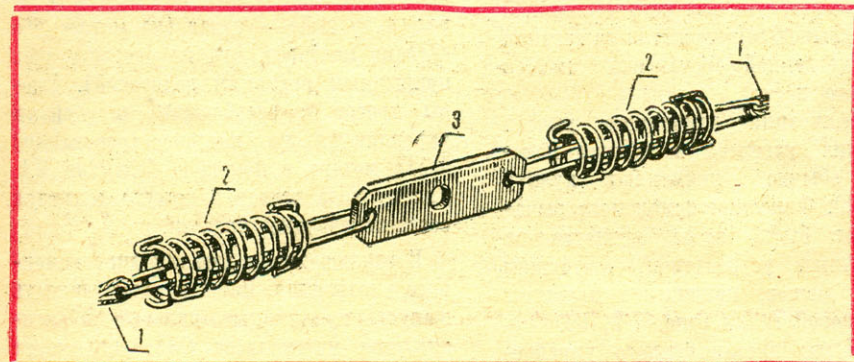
Общий вид устройства для быстрого соединения штуртросов с мотором:
